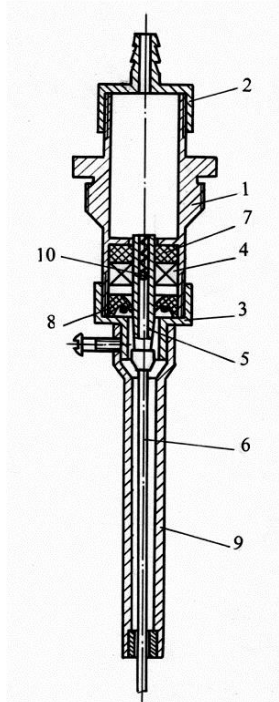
Прибор для отбора проб жидкости из вращающегося барабана сепаратора: 1 – корпус; 2, 3 – крышки; 4 – подшипник; 5 – полый вал; 6 – пробоотборная трубка; 7, 8 – уплотнения; 9 – наконечник; 10 – обратный клапан
